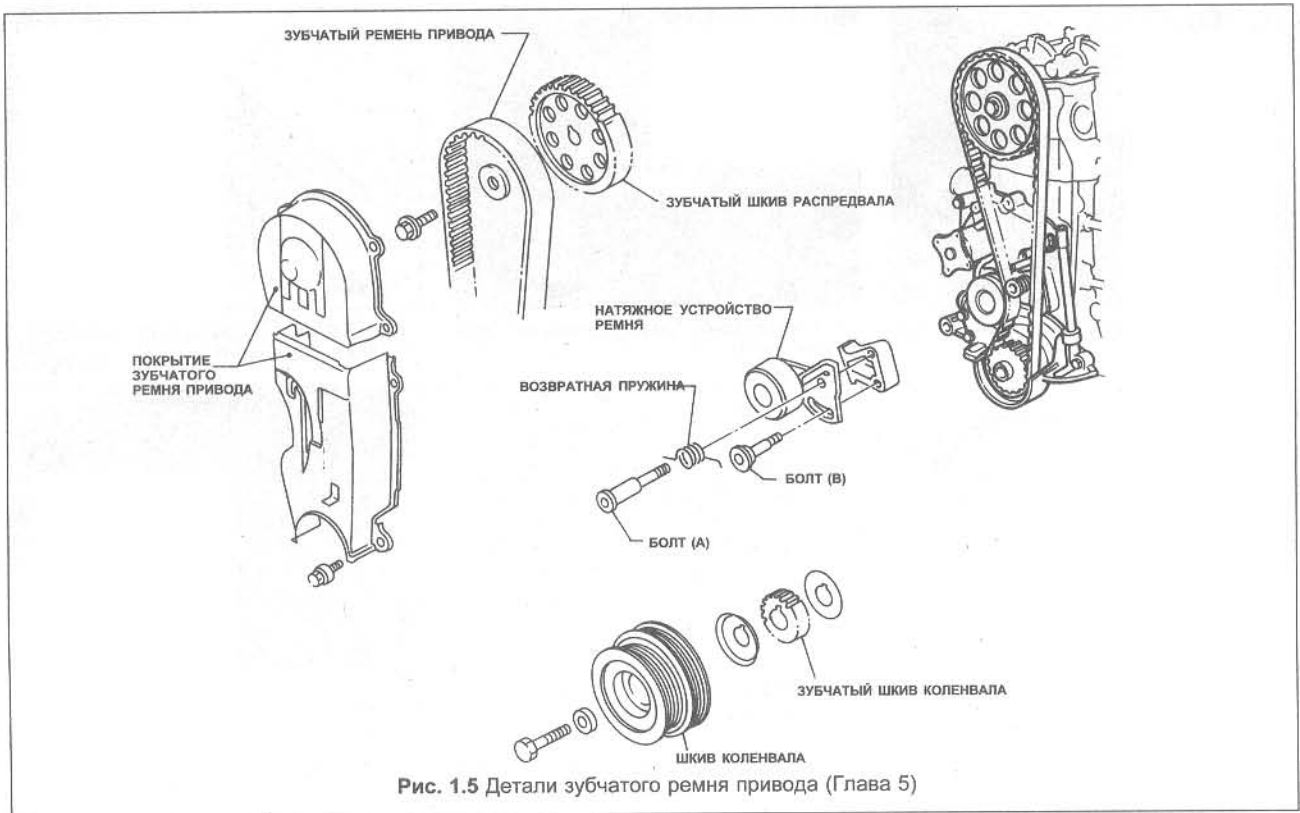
Детали зубчатого ремня привода (Глава 5)
